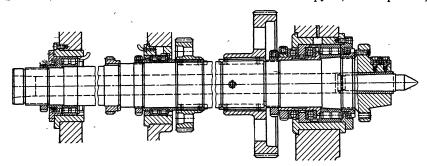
Подшипники качения в опорах шпинделя быстроходного тяжелого токарного станка
